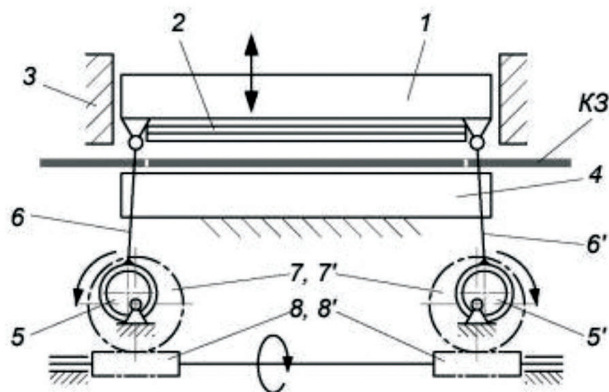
Плоский штанцювальний прес з черв'ячним механізмом привода натискної плити
